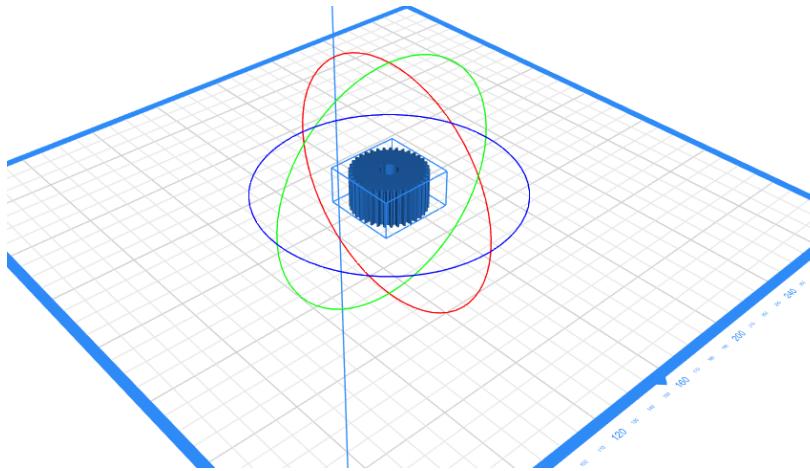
Rotación del engranaje, Fuente: El Autor
